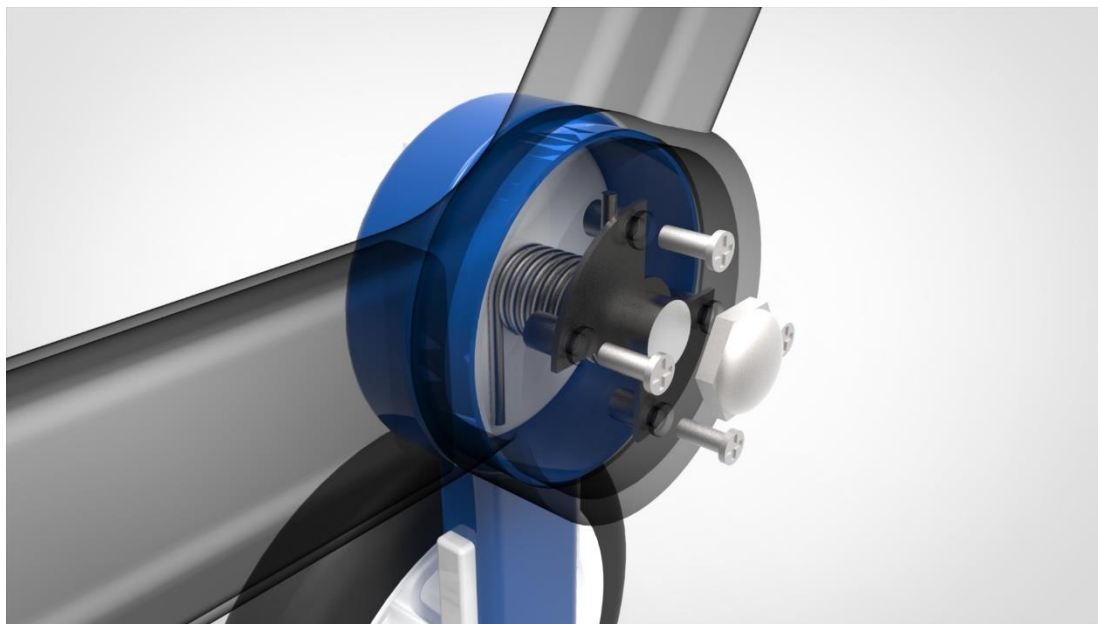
vista explodida e em perspectiva do sistema de repouso
